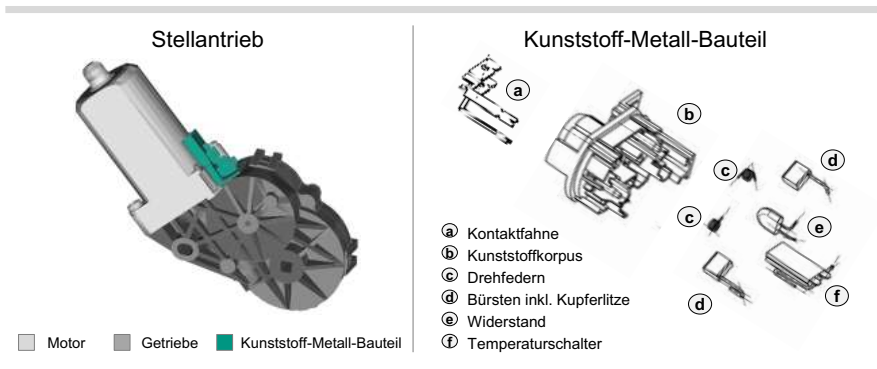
Stellantrieb und Explosionszeichnung des Kunststoff-Metall-Bauteils
